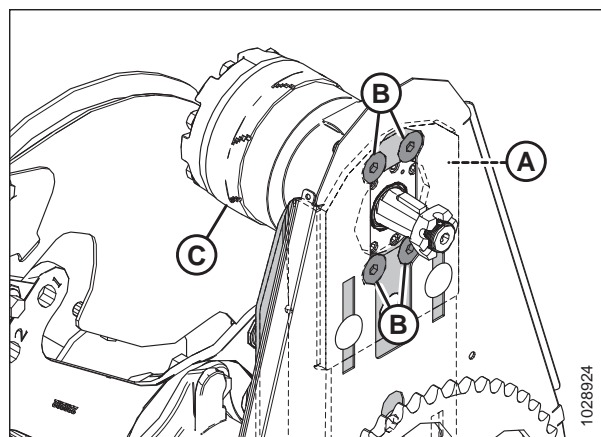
Винты крепления гидромотора привода мотовила
